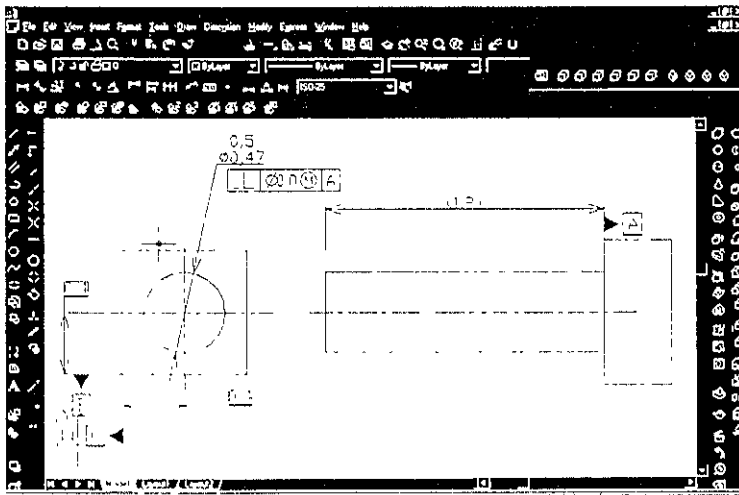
Eje sólido (usando *tolerancias y dimensiones geométricas*)
